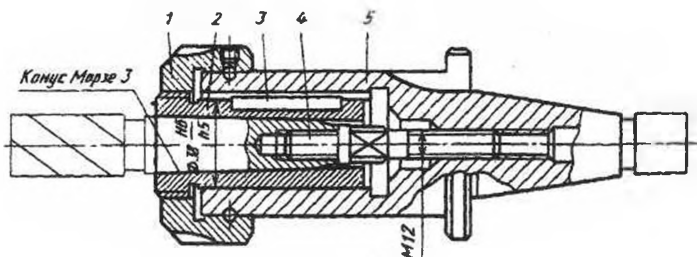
Патрон для кріплення фрез з конічним хвостовиком
